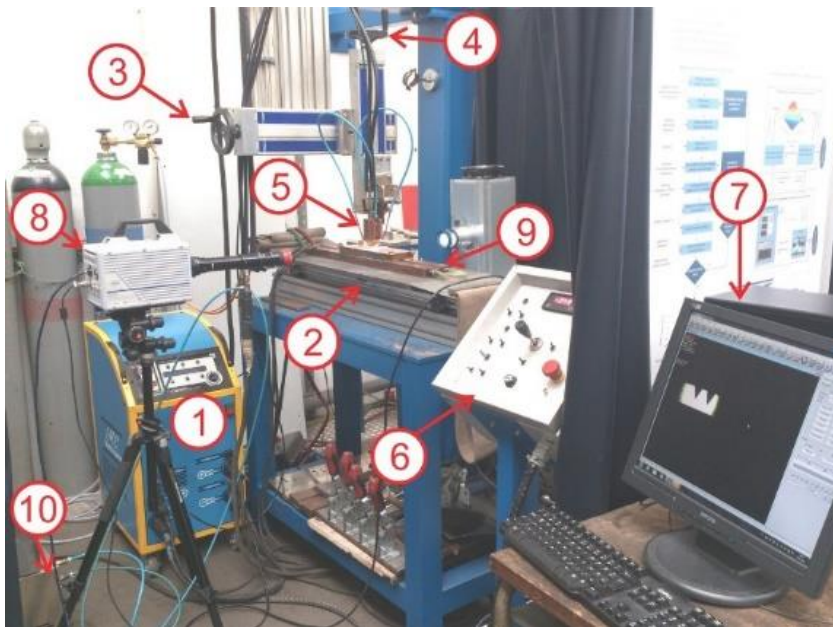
Imagem da bancada de soldagem TIG duplo eletrodo no ISF-RWTH-Aachen
